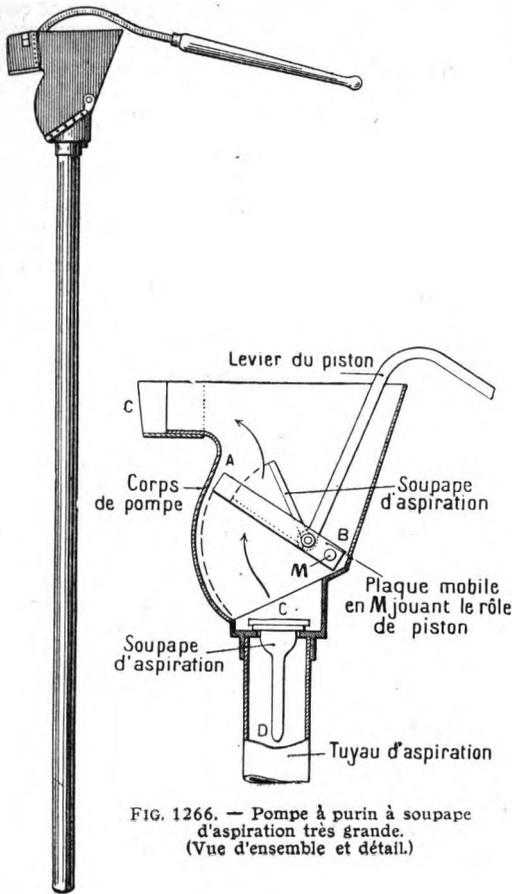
Pompe à purin à soupape d'aspiration très grande. (Vue d'ensemble et détail.)
